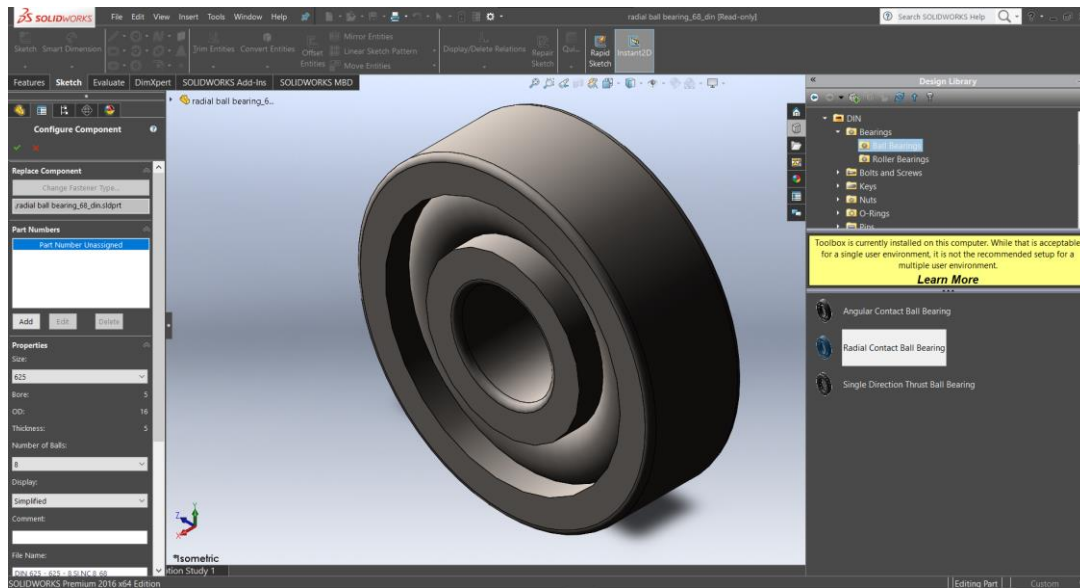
Створення підшипника із бібліотеки стандартних деталей Toolbox
